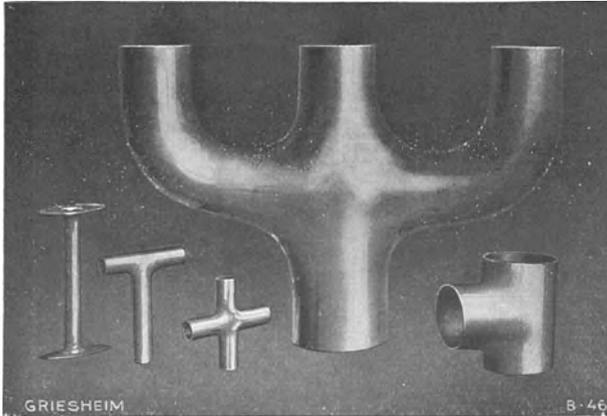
Geschweißte Aluminiumformstücke.
